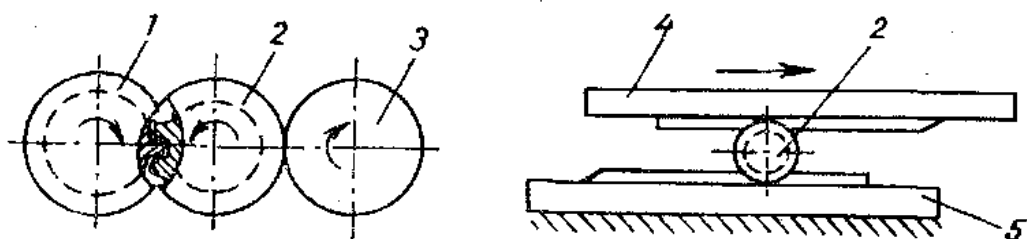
Схеми накатування спеціальних поверхонь циліндричним і плоским інструментами:
